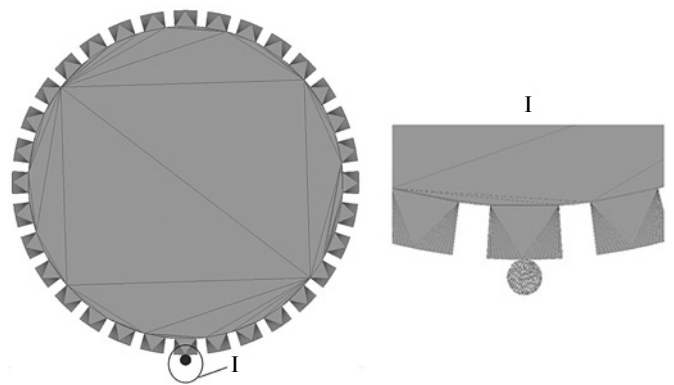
Модель контакта заготовки и пилы и начальный момент входа зуба в заготовку (I)
